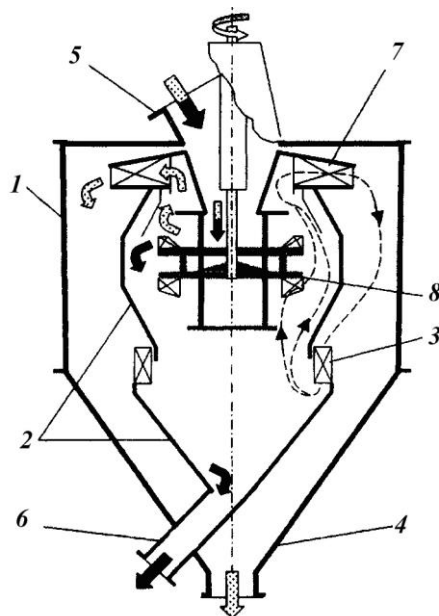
Циркуляційний відцентровий класифікатор «Вентоплекс»: 1 – зовнішній корпус; 2 – внутрішній корпус; 3 – лопатки; 4 – розвантажувальний патрубок дрібного продукту; 5 – завантажувальний патрубок; 6 – розвантажувальний патрубок великого продукту; 7 – вбудований вентилятор; 8 – розподільна тарілка
